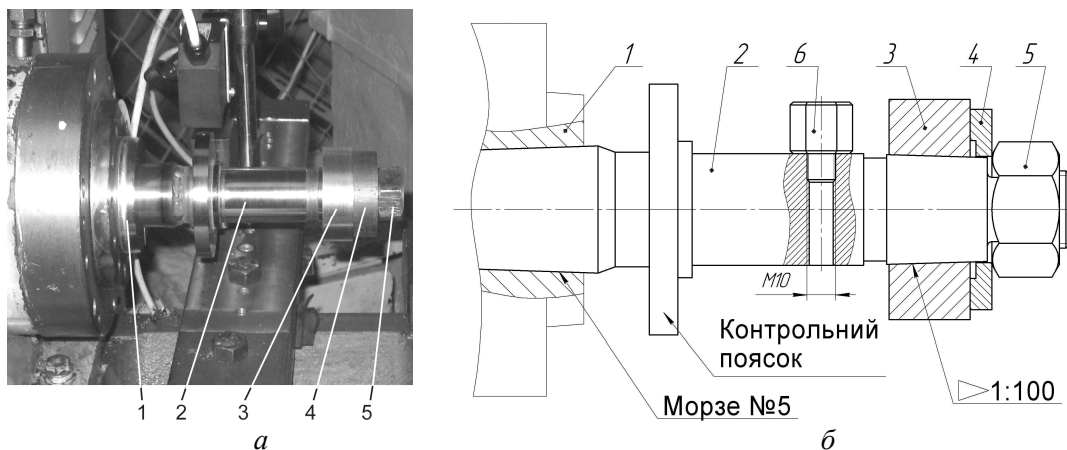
До опису конструкції та схеми закріплення прецизійної оправки: 1 – шпindelь; 2 – прецизійна оправка; 3 – оброблювана заготовка; 4 – шайба; 5 – гайка; 6 – змінний вантаж
